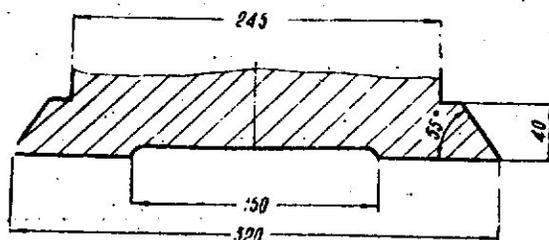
Эскиз направляющих станка модели 6М82Ш
